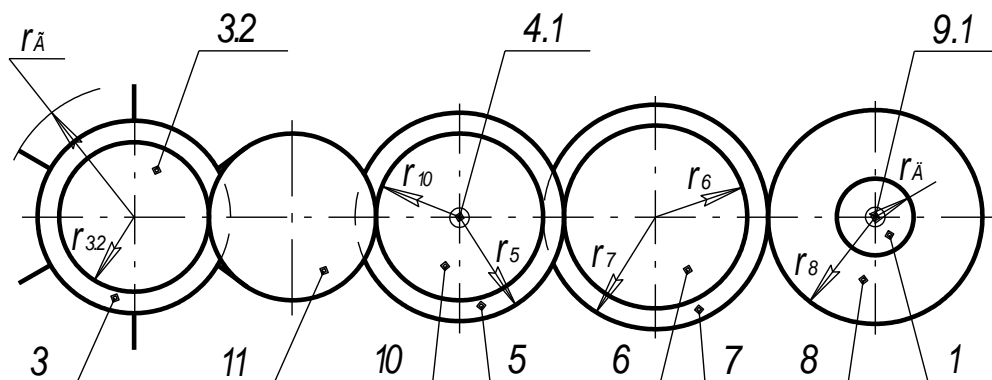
Упрощенная развернутая схема зубчатых передач станка
